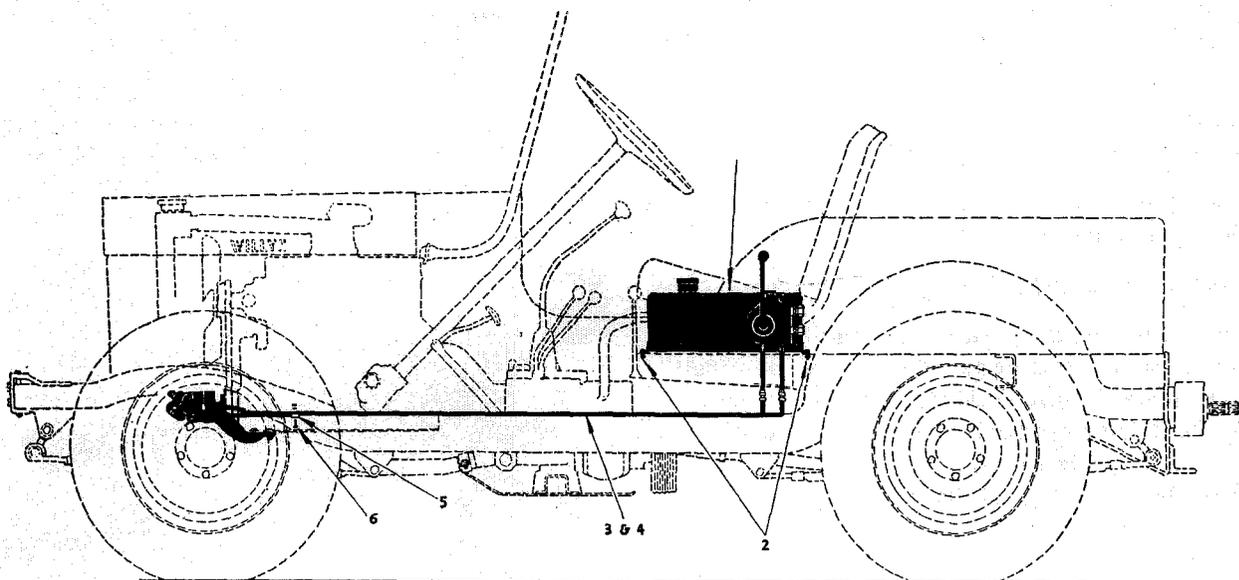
Einbau der hydraulischen Leitungen unter dem Jeep
